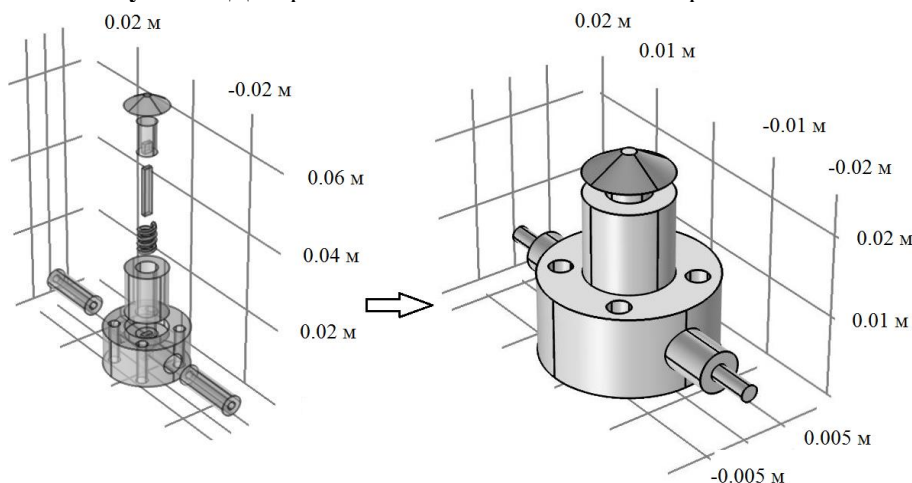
Схема сборки датчика и внешний вид готового изделия.
